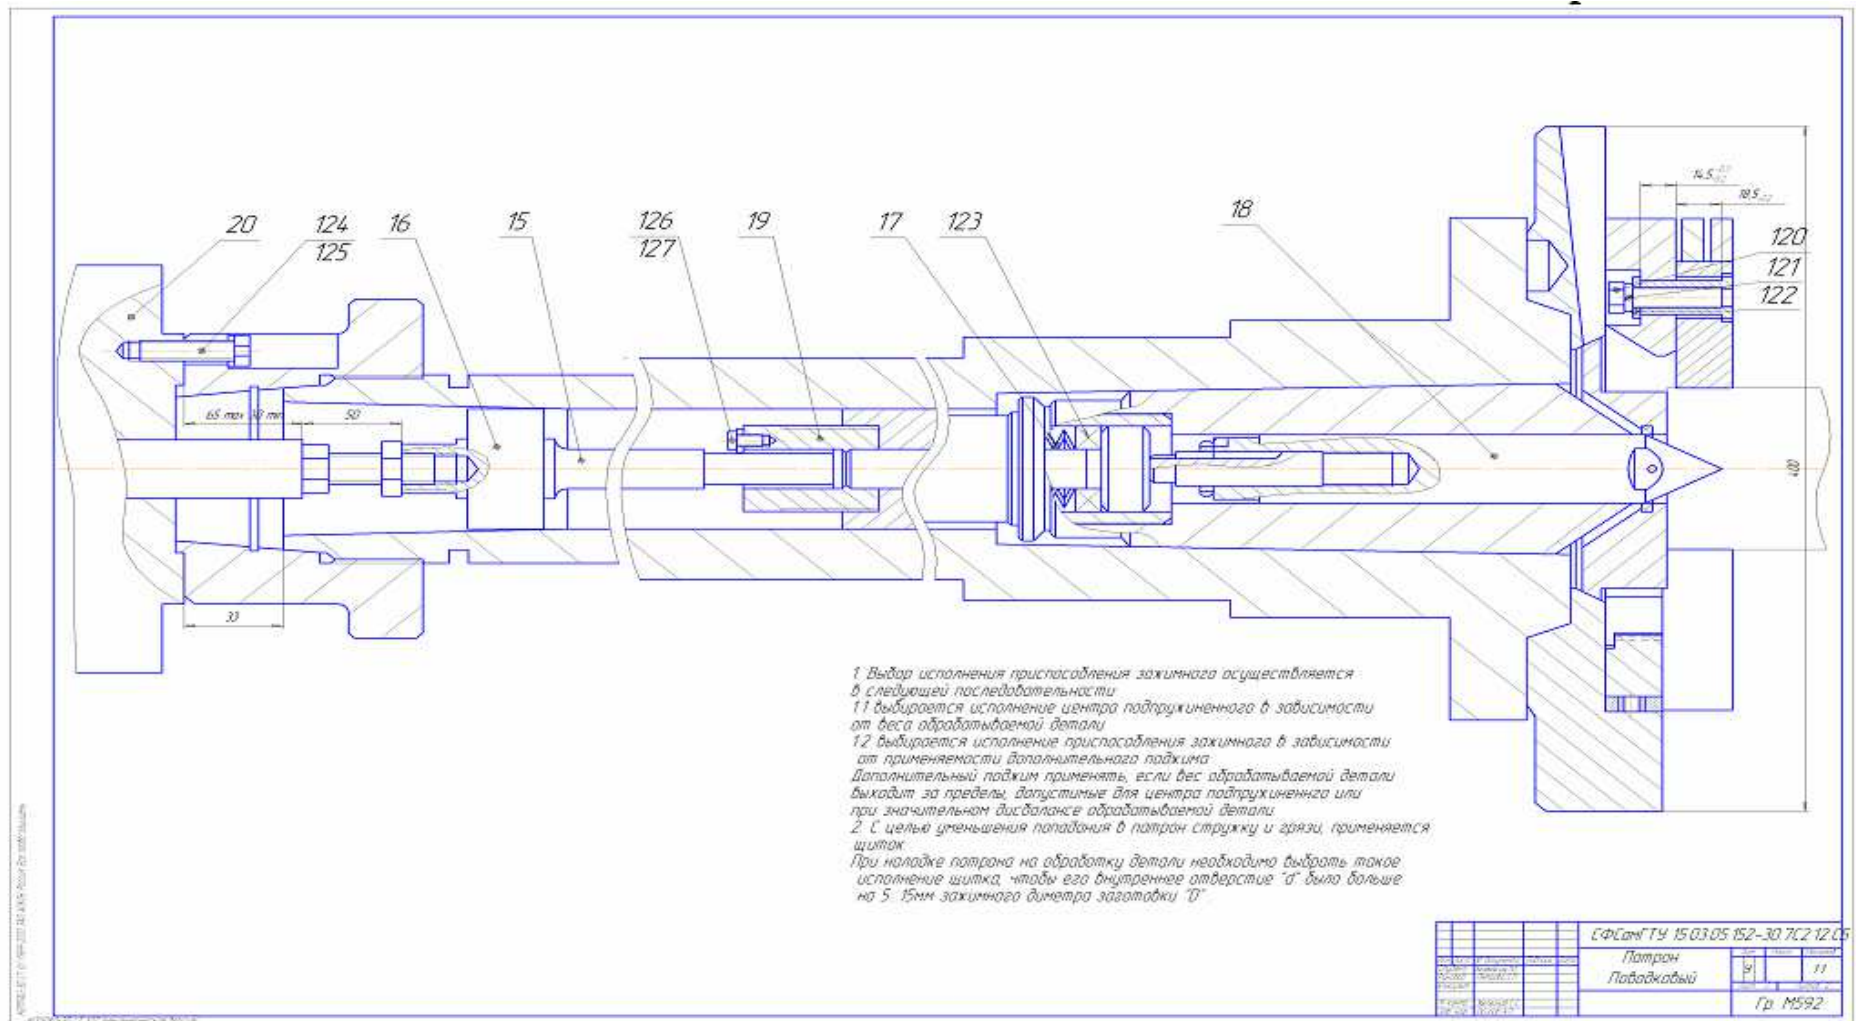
Пример выполнения чертежа станочного приспособления
